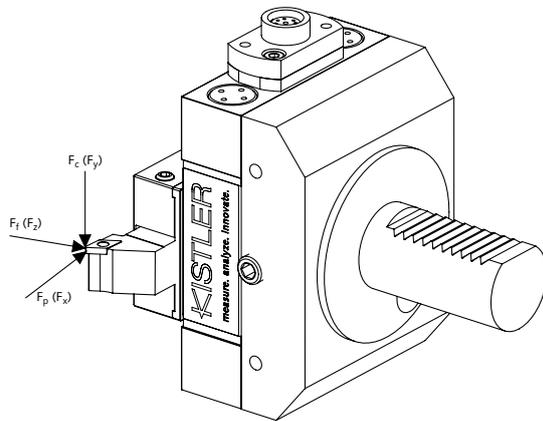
Dynamometer Typ 9119AA2 mit Werkzeughalter Typ 9119AE16 und VDI-Werkzeugaufnahme Typ 9119AB30S
